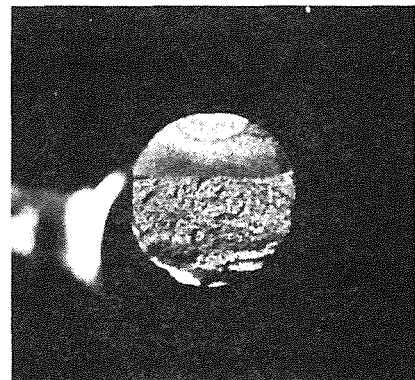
Superfície de fractura dum provete de $\phi=14$ mm, em flexão alternada com torção.
